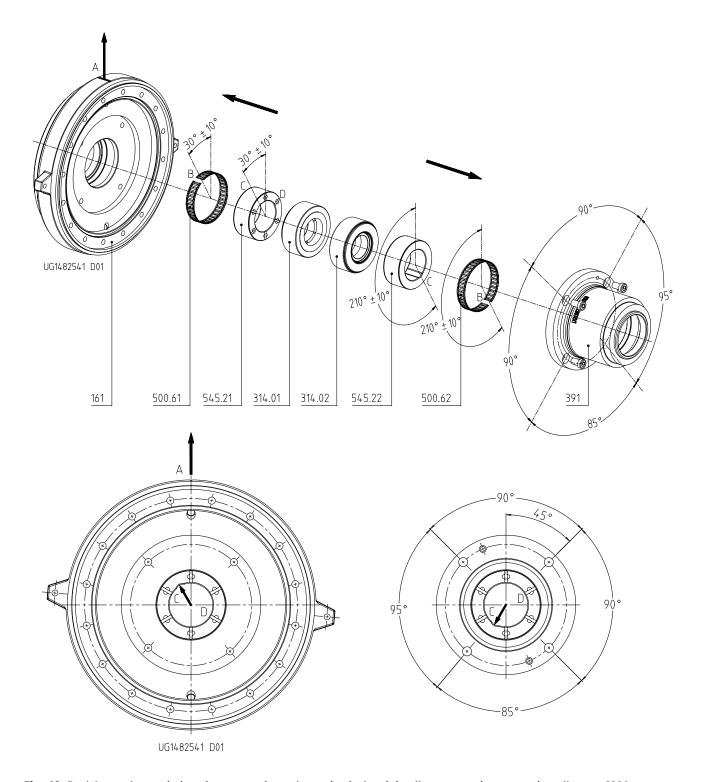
Posicionamiento de los elementos de apriete y los bujes del cojinete con el soporte de cojinetes CS80
